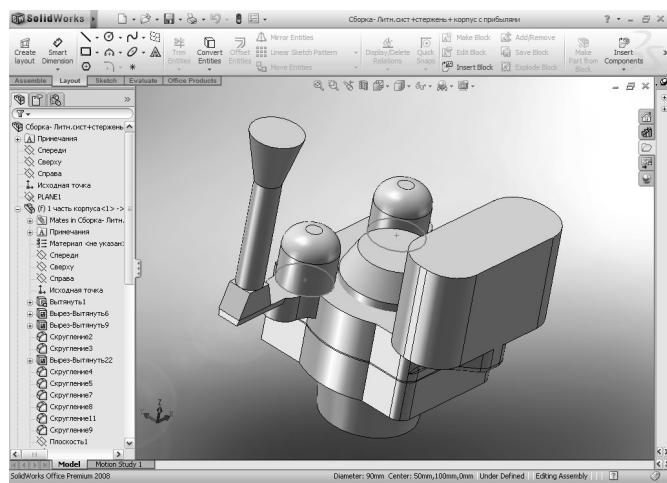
3D-модель отливки в сборке со стержнем, литниковой системой и прибылями
